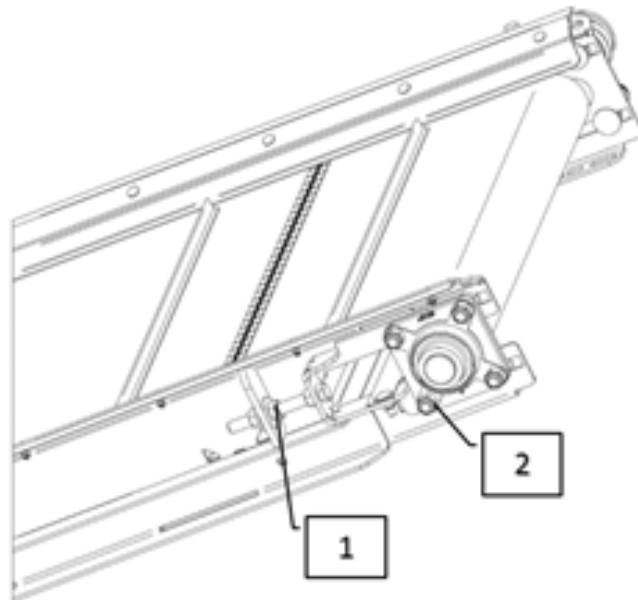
Réglage de la tension du tapis du convoyeur horizontal ou incliné
